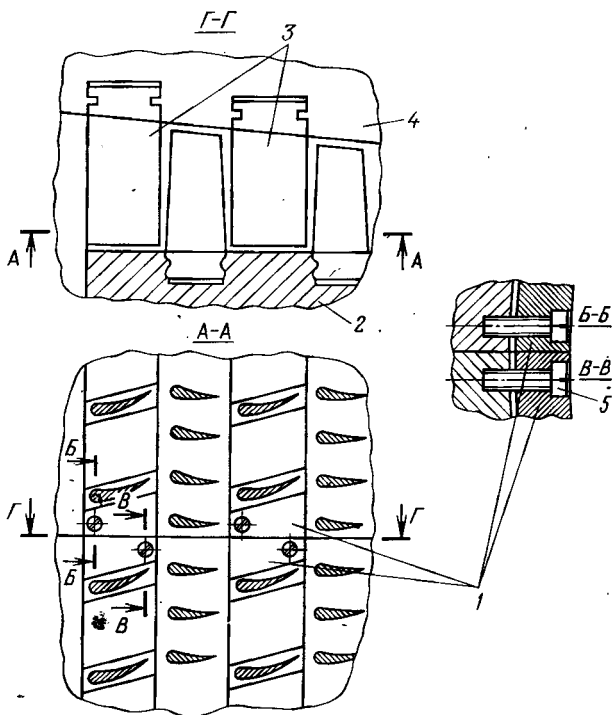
Направляющие лопатки и их крепление у горизонтального разреза корпуса:
